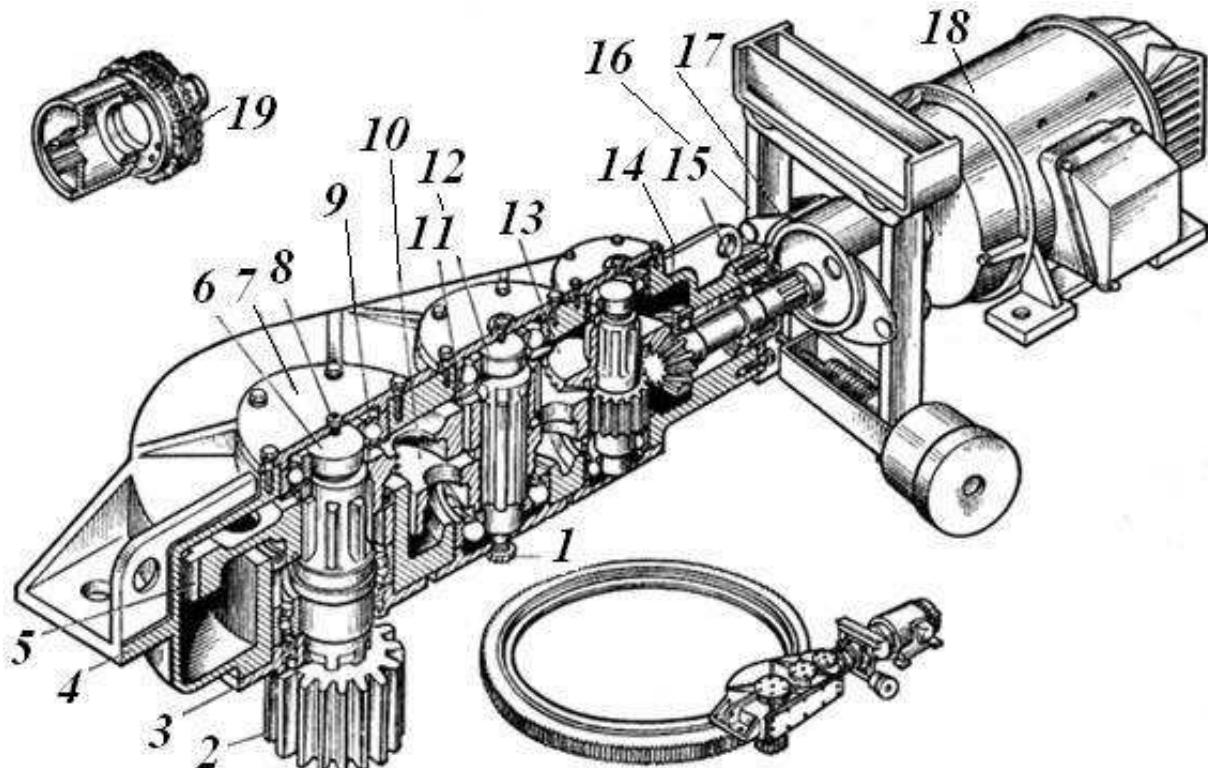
Общий вид механизма поворота: 1 – пробка, 2, 11 – шестерни, 3, 7 – крышки, 4 – корпус редуктора, 5, 10, 13 – зубчатые колеса, 6 – вертикальный вал, 8 – масленка, 9, 15 – подшипники, 12 – вал, 14 – вал-шестерня, 16 – тормоз, 17 – шкив, 18 - электродвигатель, 19 – цепная муфта
